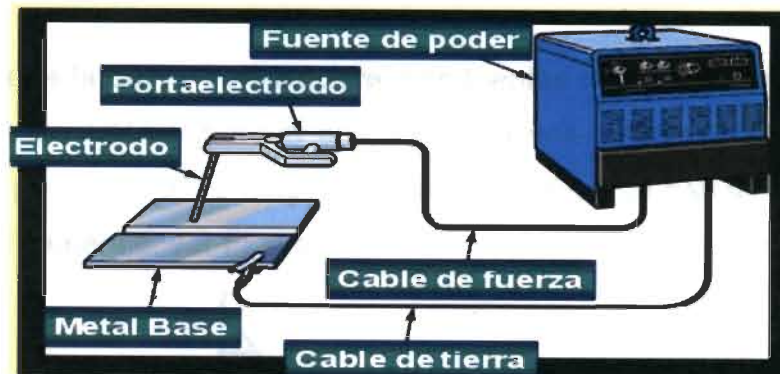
Diagrama de Equipo Básico de Soldadura (5).
